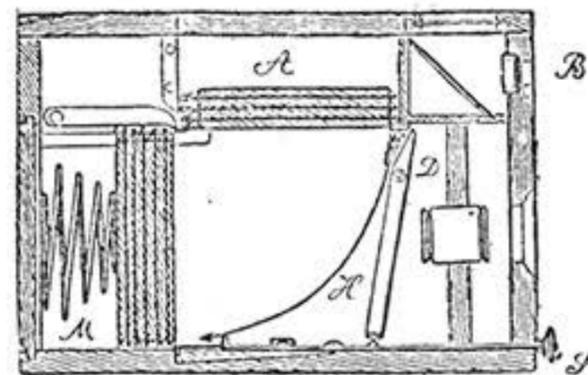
Приспособление для смены пластинок в магазинной камере.
